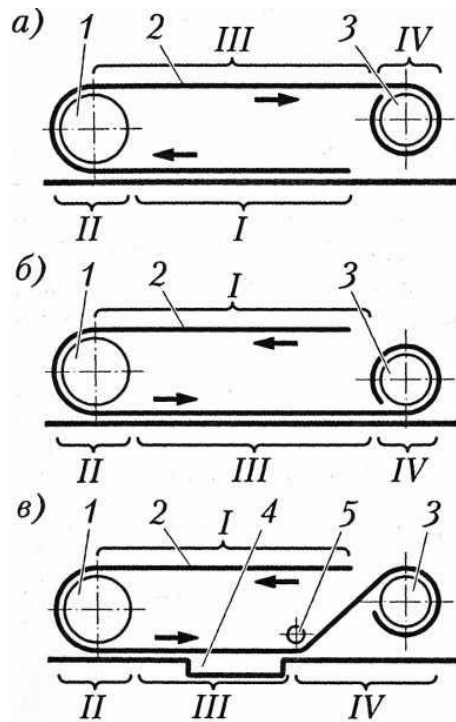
Компонувальні схеми двоярусних установок для виготовлення зварних полотнищ в рулонах [1]:
